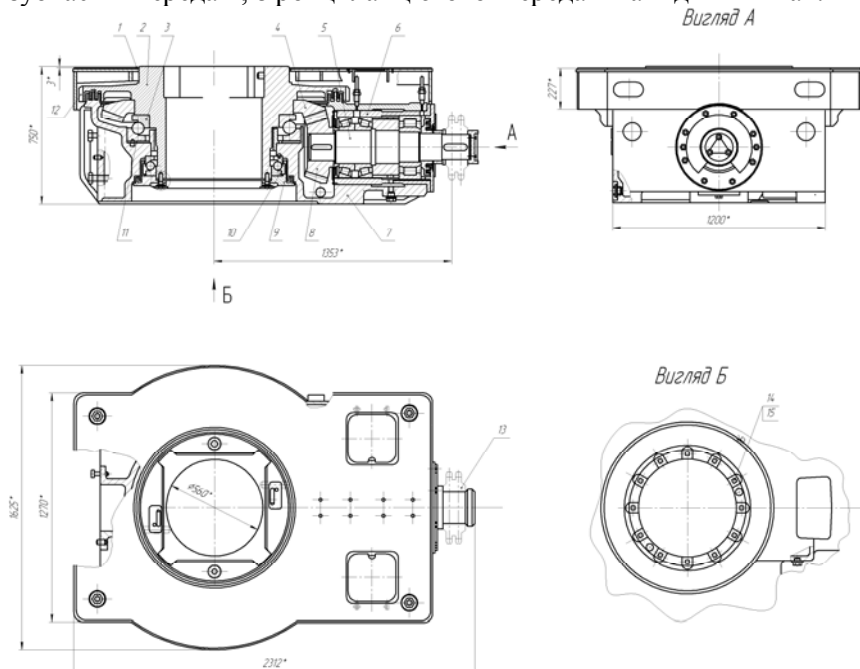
Ротор: 1 – кришка; 2 – стіл ротора; 3 – основна опора; 4 – конічне колесо; 5 – швидкохідний вал; 6 – стакан; 7 – станина; 8 – конічна шестірня; 9 – фланець; 10 – допоміжна опора; 11 – регулювальне кільце; 12 – фіксатор; 13 – зубчасте колесо; 15 – планка опорна
